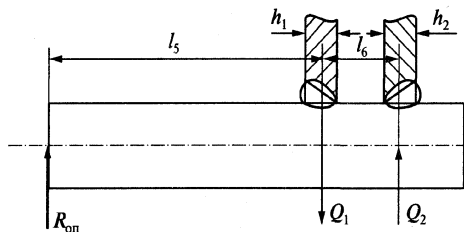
Расчетная схема определения напряжений в сварных швах цапфы
